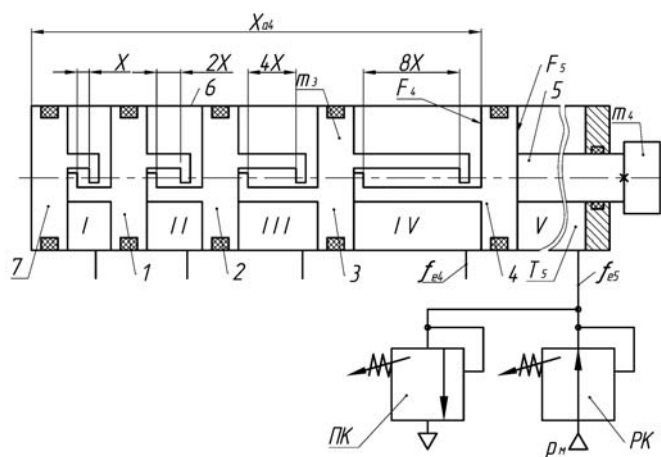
Розрахункова схема пневматичного цифрового приводу
